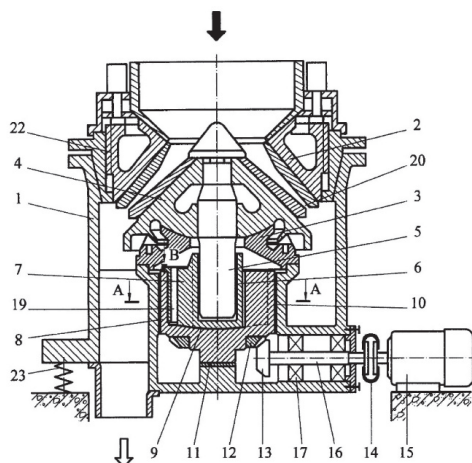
Конструктивная схема дробилки из патента RU91007U1: 1 — корпус; 2 — наружный конус; 3 — сферическая опора; 4 — внутренний конус; 5 — главный вал; 6, 17 — подшипники; 7 — приводной эксцентрик; 8 — подшипниковая втулка; 9 — сферическая пята; 10 — радиальный подшипник; 11 — упорный подшипник; 12 — зубчатое колесо; 13 — шестерня; 14 — эластичную муфту; 15 — электродвигатель; 16 — горизонтальный; 18 — эксцентричная поверхность; 19 — минимальный зазор; 20 — максимальный разгрузочный зазор; 21 — серповидный вкладыш; 22 — резьба; 23 — упругие амортизаторы
